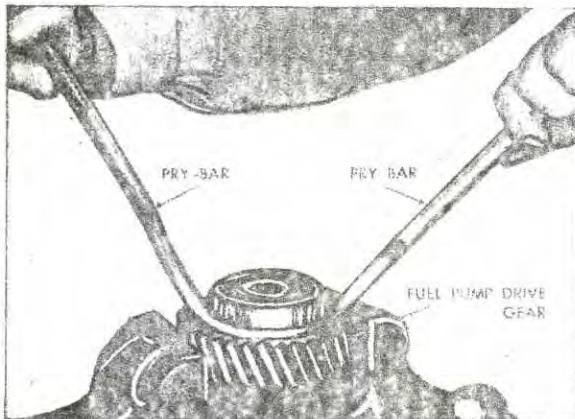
Desmontaje del cojinete de bolas del engranaje impulsor tipos sin compresor.
